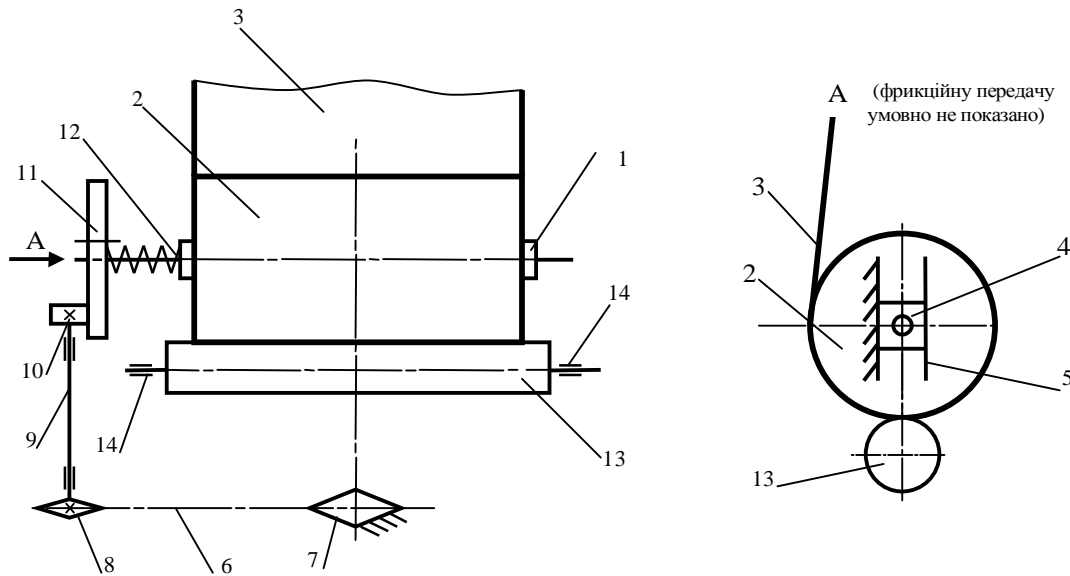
Кінематична схема механізму намотування полотна з лобовим фрикційним варіатором: 1 – товарний валик; 2 – рулон полотна; 3 – полотно; 4 – повзуні; 5 – направляючі; 6 – ланцюгова передача; 7, 8 – зірочки; 9 – вал; 10, 11 – відповідно ролик та диск варіатора; 12 – пружина; 13 – опорний валик; 14 – підшипники опорного валика
